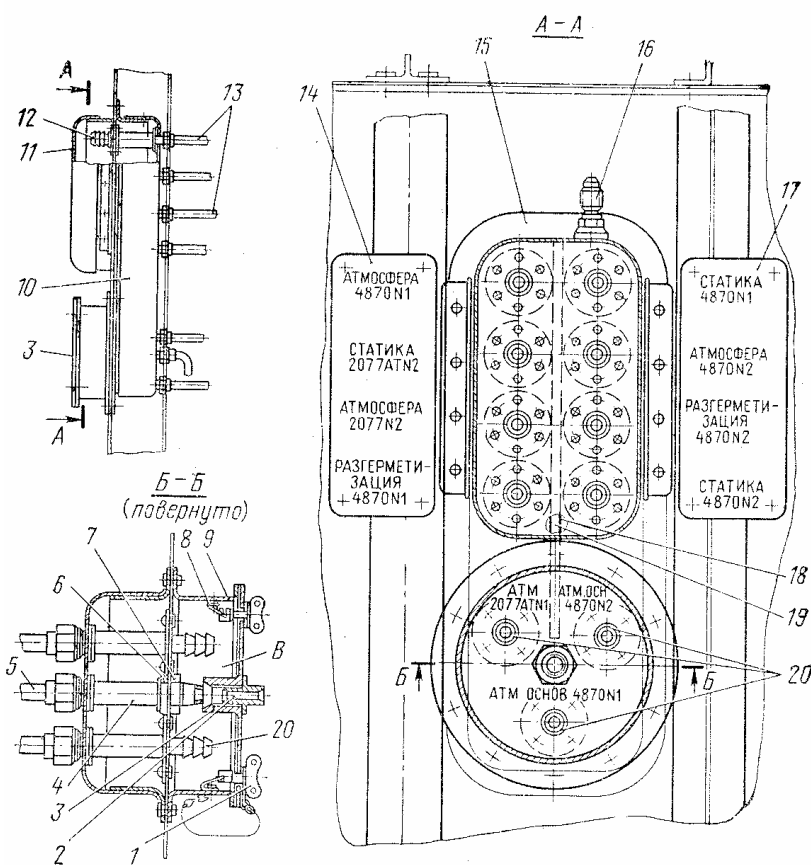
Камера разрежения и кожух обогрева бортовых иштуцеров:
